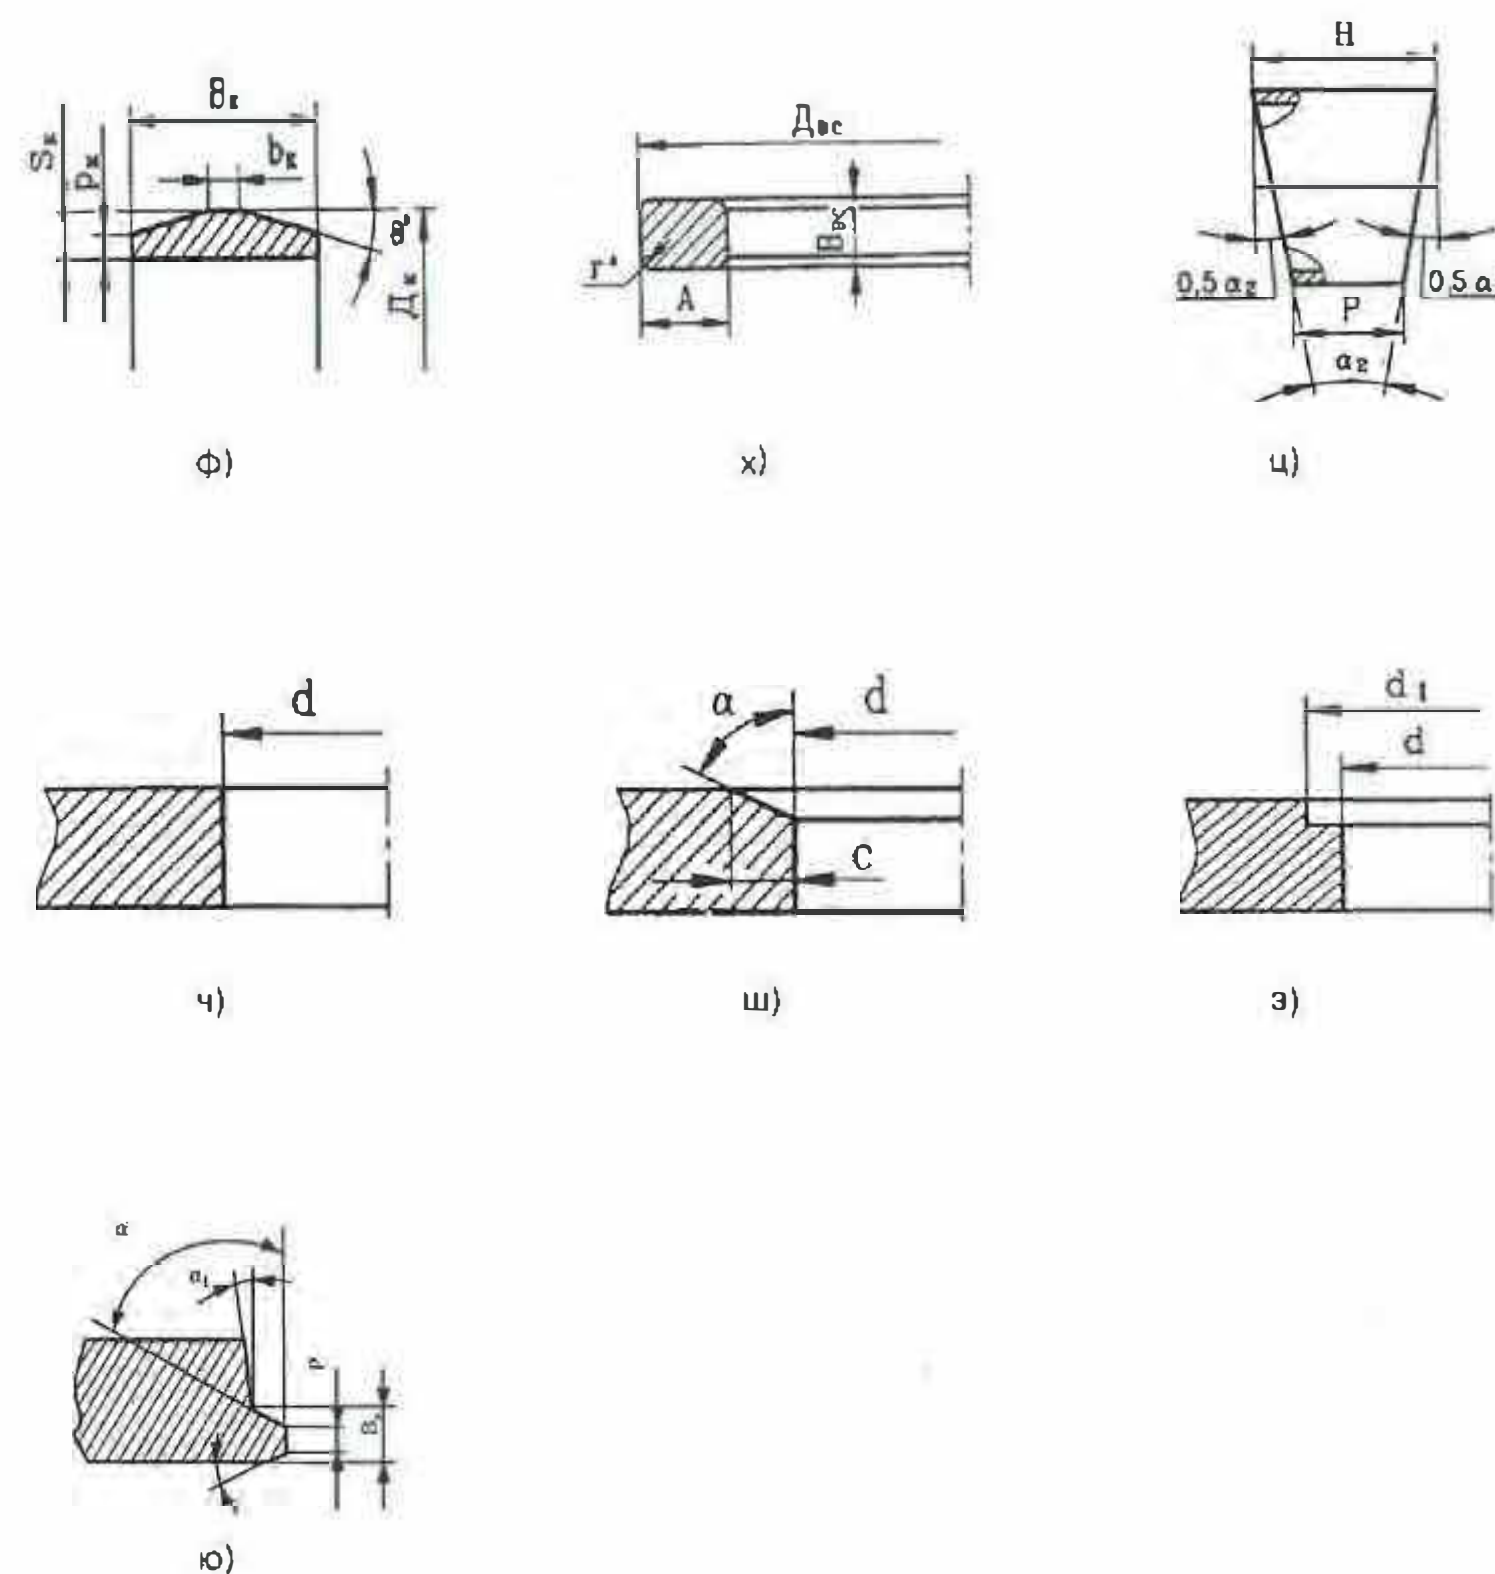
лист 3. Размеры, контролируемые измерением при подготовке деталей под сварку
